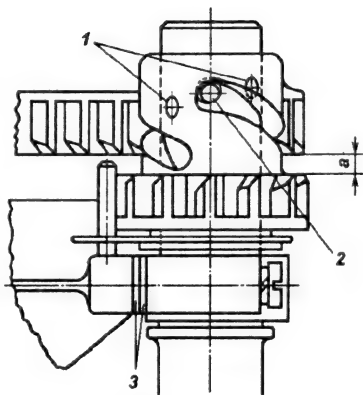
Регулировка зазора шестерни пускового механизма в зацеплении с маховиком
